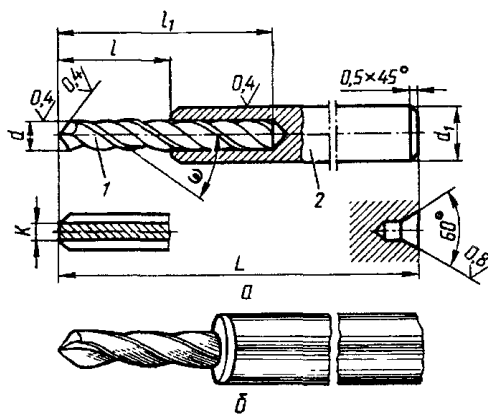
Твердосплавне суцільне спіральне свердло: а - креслення; б - загальний вигляд; 1 - цілісна твердосплавна спіральна коронка; 2 - оправка
